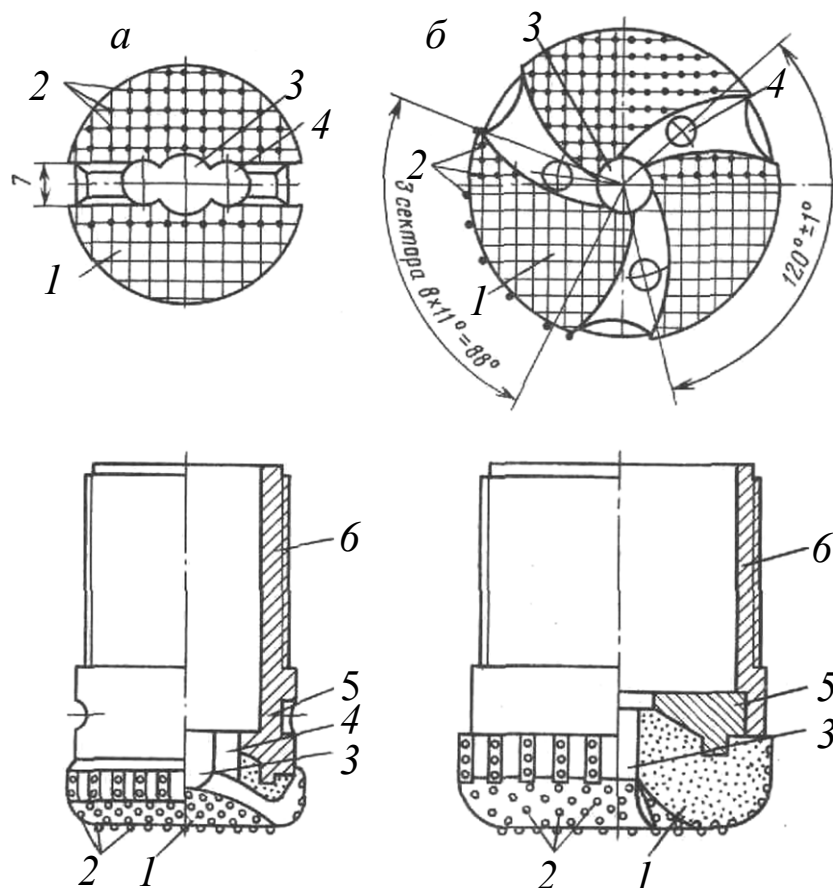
Конструкции однослойных долот: 1 – матрица; 2 – торцовые резцы; 3 – центральный промывочный канал; 4 – боковые промывочные каналы; 5 – корпус долота; 6 – присоединительная резьба
